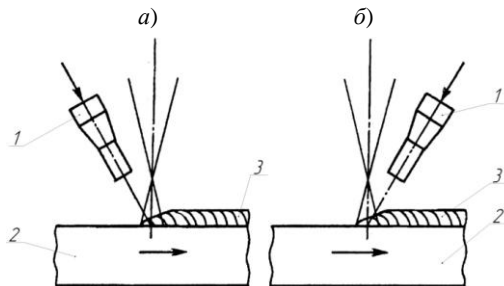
Схемы лазерной газопорошковой наплавки с подачей порошка вслед (а) и навстречу (б) движению детали: 1 – лазер; 2 – деталь; 3 – наплавленный слой
